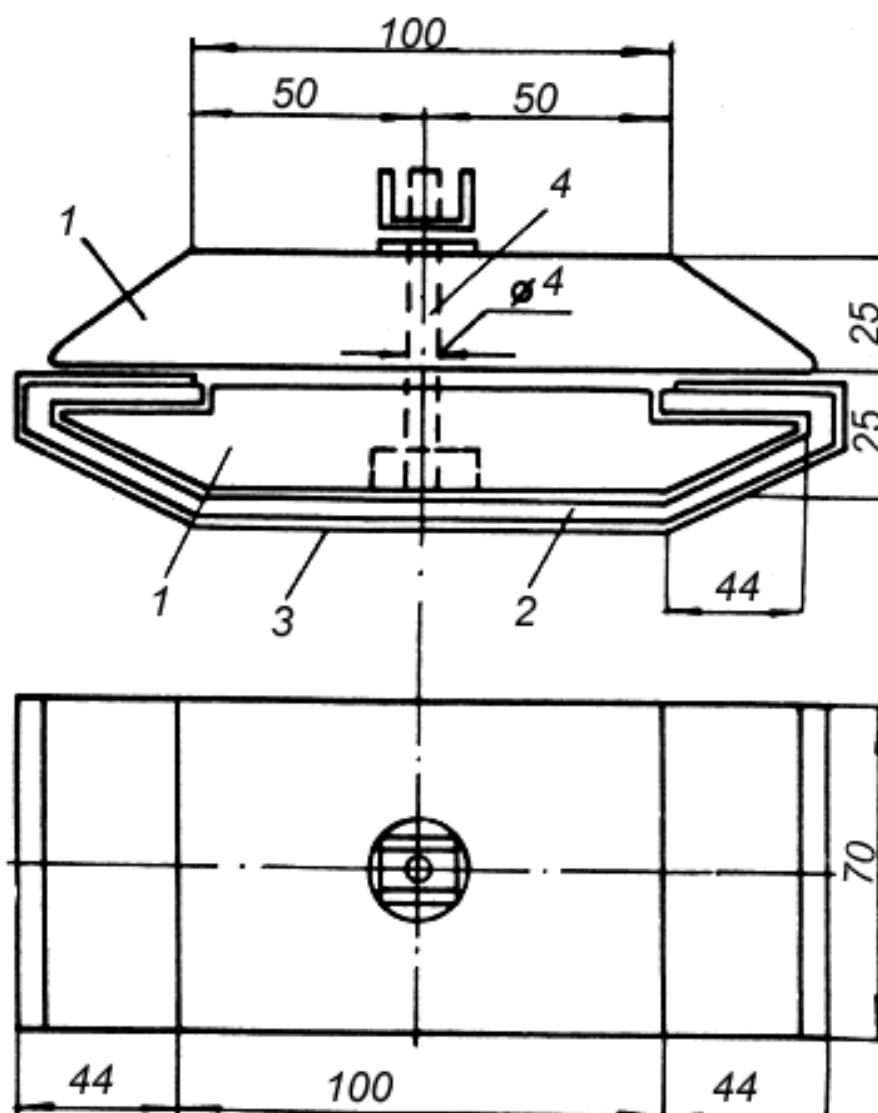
Деревянная колодка для крепления шлифовальной шкурки
